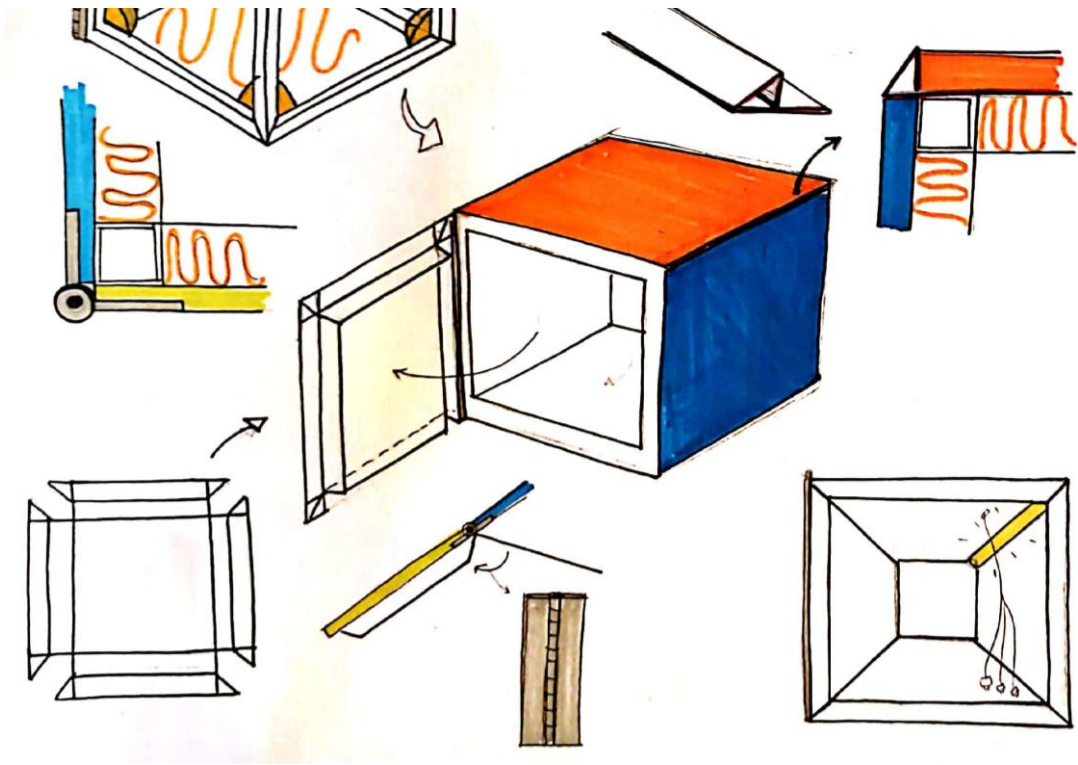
Conjunto de croquis explicativos - Elaboración propia
